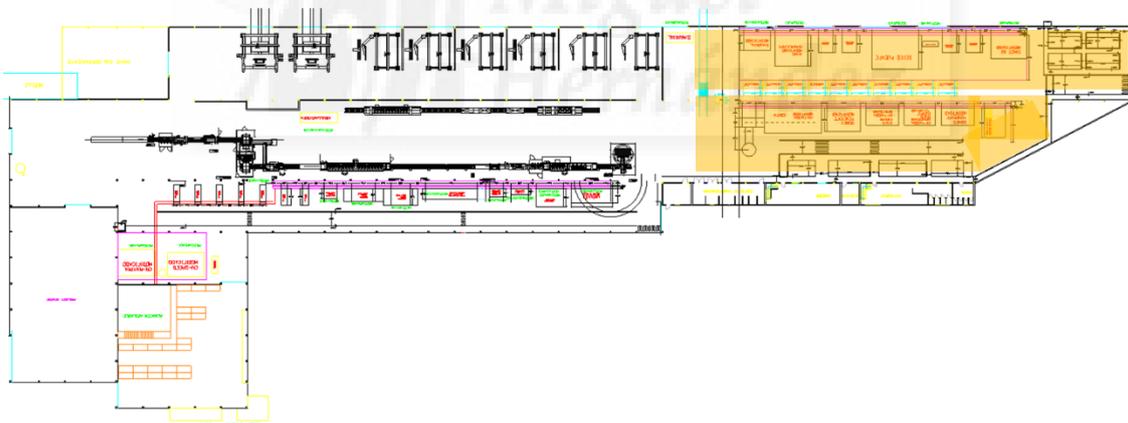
Sección de Corte. (PIEDRA NATURAL SL, 2016)
